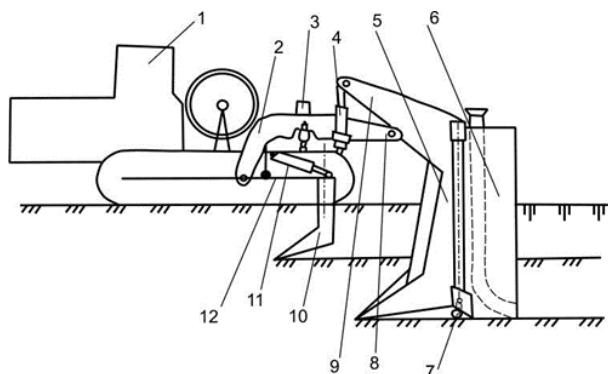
Дослідний зразок робочого органу дреоукладача (другий варіант): 1 – базова машина; 2 – тягова рама; 3, 4, 11 – гідроциліндри; 5 – основний ніж; 6 – трубоукладач; 7 – шарнір з'єднання основного ножа з трубоукладачем; 8 – шарнір з'єднання коромисла з тяговою рамою; 9 – коромисло; 10 – додатковий ніж; 12 – тягова рама додаткового ножа
